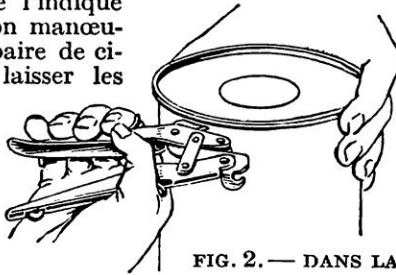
DANS LA FENTE ON ENGAGE LA LAME DE LA CISAILLE, PUIS ON DÉCOUPE RÉGULIÈREMENT SOUS LE COUVERCLE
